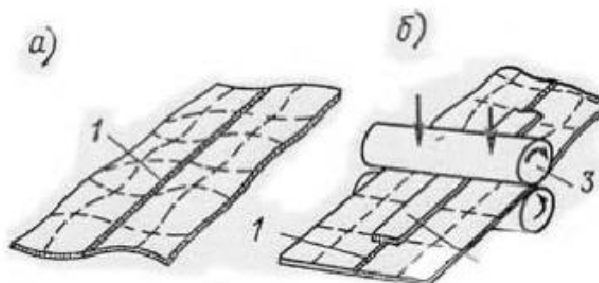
Схема исправления деформированных изделий из тонколистового металла *a* – листы после сварки до прокатки, *б* – схема процесса прокатки, *1* – сварной шов, *2* – накладка, *3* – прокатные валки
